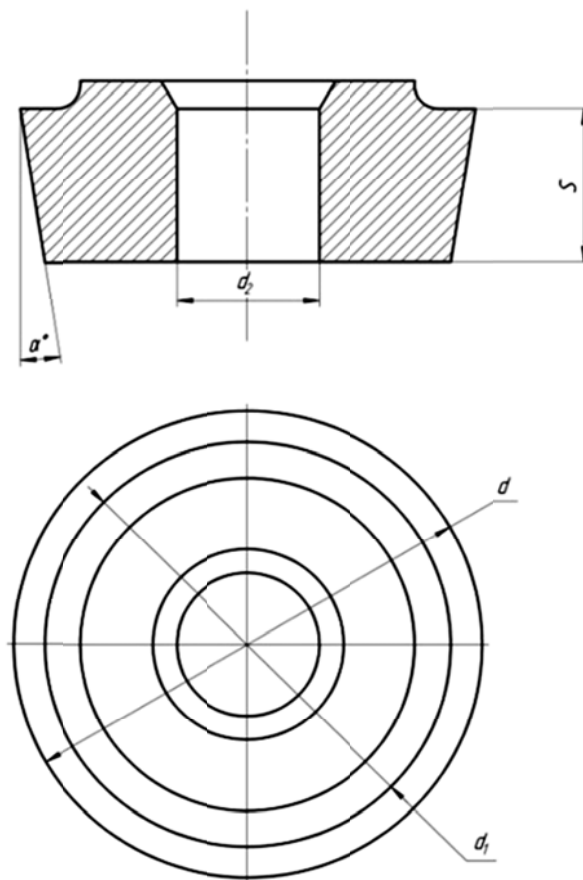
Режущая пластина исследуемого сборного чашечного резца
